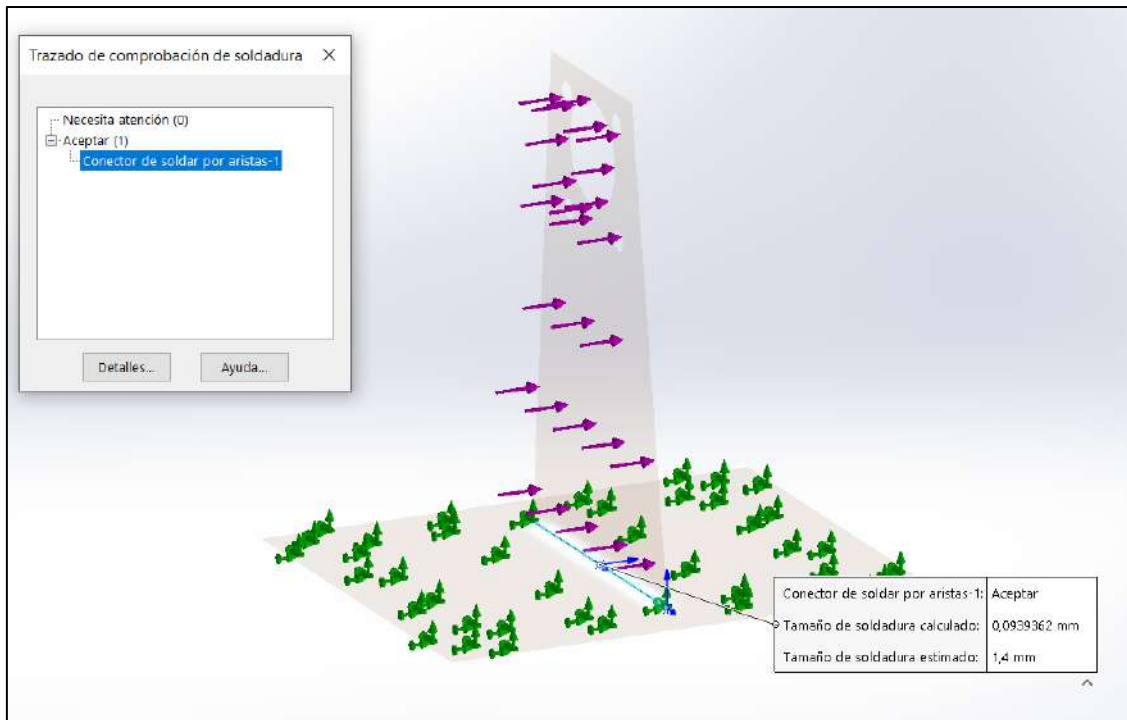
Trazado de comprobación de soldadura.
